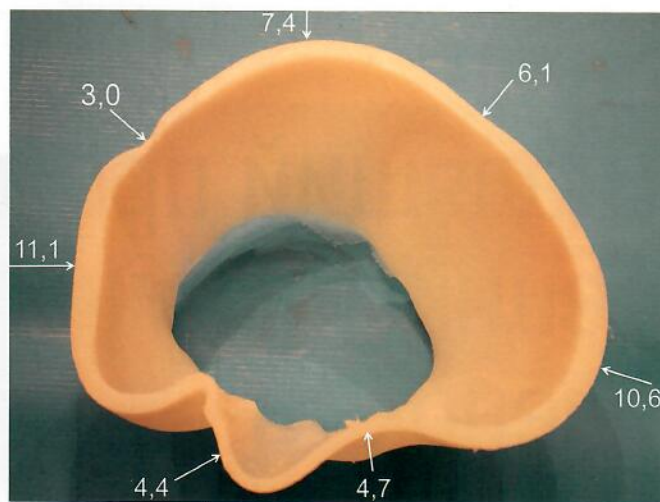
Распределение толщины стенки заготовки, необходимое для того, чтобы обеспечить возможность изготовления детали методом выдувного формования
